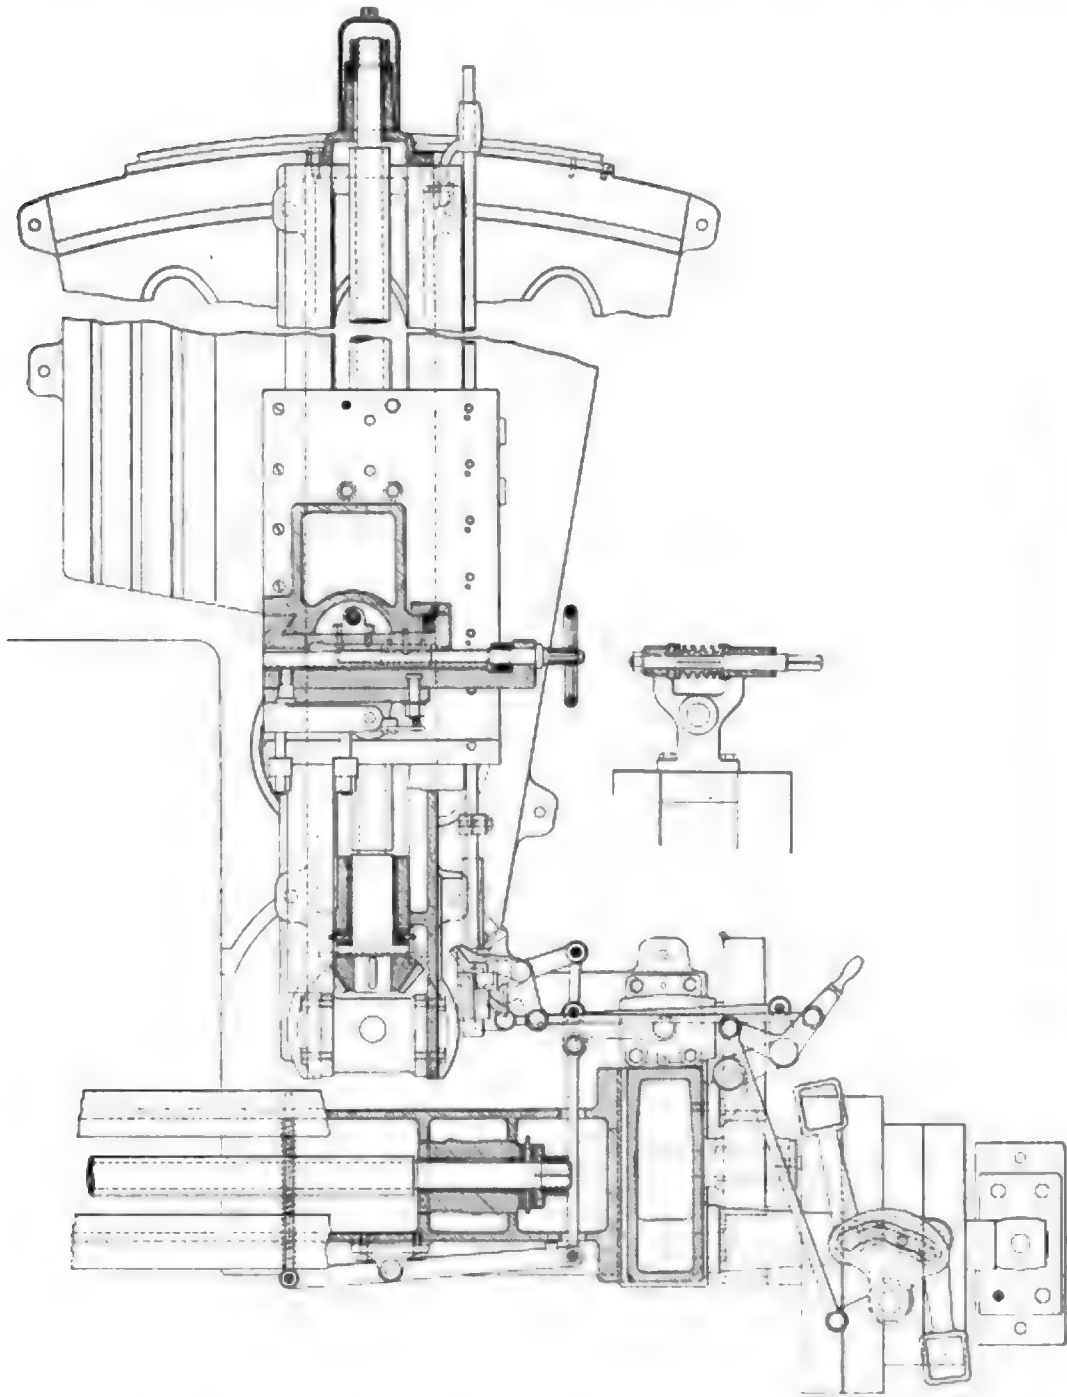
Blechkantenhobelmaschine (Deutsche Nileswerke)
